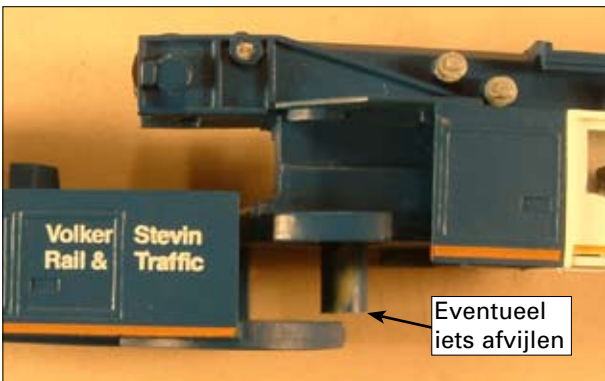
frame incl. onderdelen en achterzijde bovenwagen
